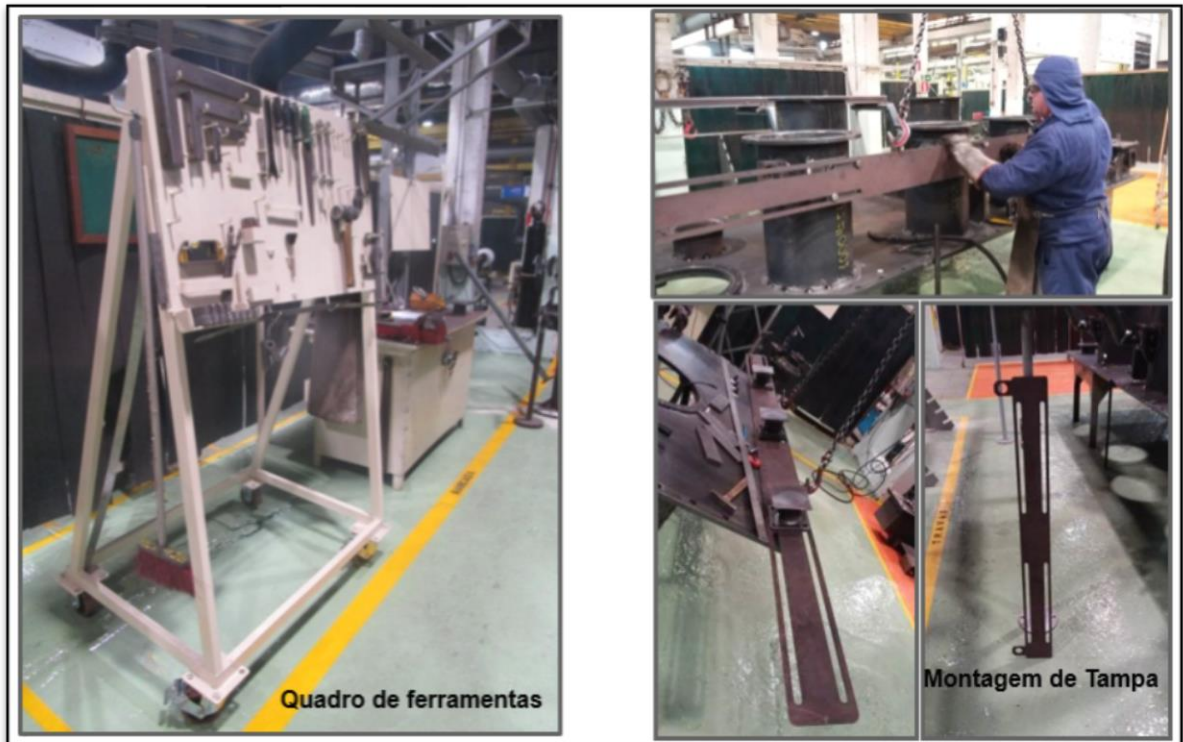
Posto de trabalho montagem e soldagem de tampa
